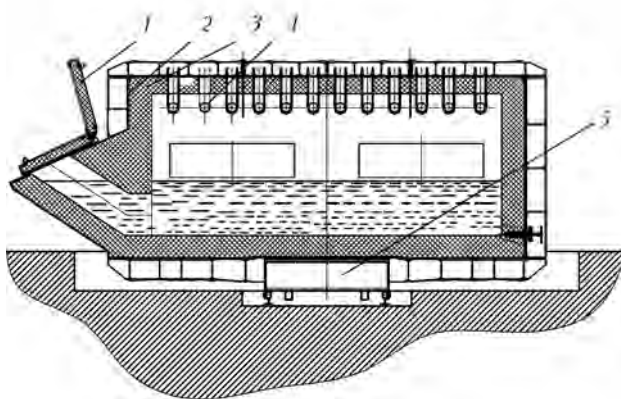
Камерная электропечь-миксер типа САМП: 1 — заливочная крышка; 2 — кожух; 3 — футеровка; 4 — нагревательные элементы; 5 — МГД перемешиватель
